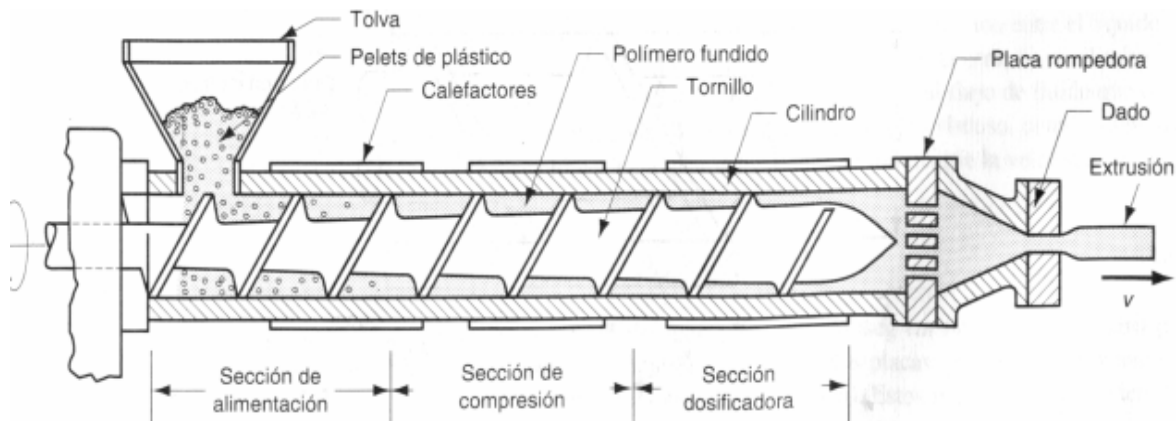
Disposición general de una máquina extrusora [tomada de GROOVER. Fundamentos de manufactura moderna]
